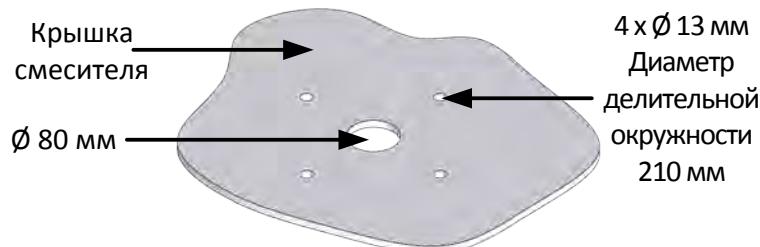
Крышка смесителя, подготовленная для вращающегося соединителя
